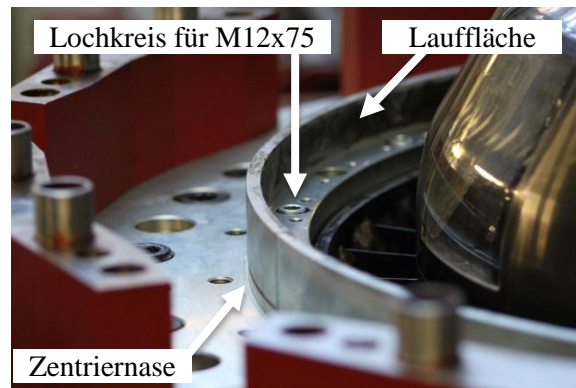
Lauffläche für O-Ring-Dichtung
